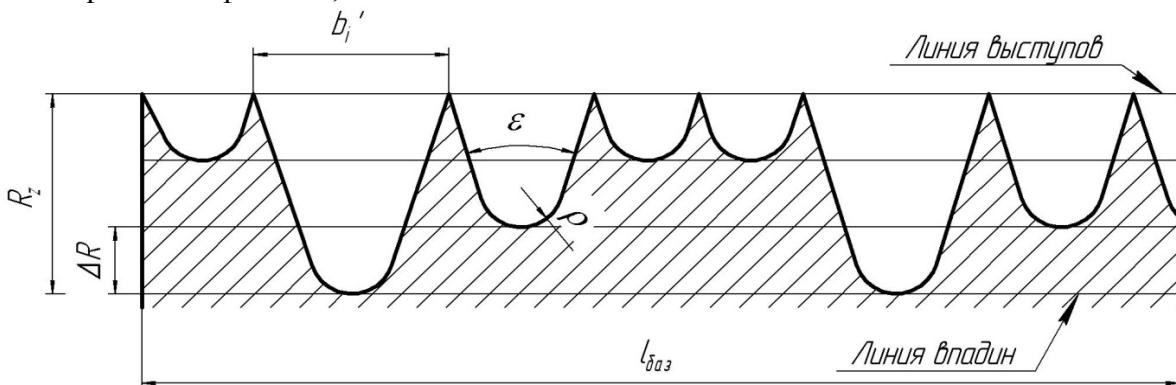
Шероховатость обработанной поверхности, сформированная единичными неперекрытыми срезами
